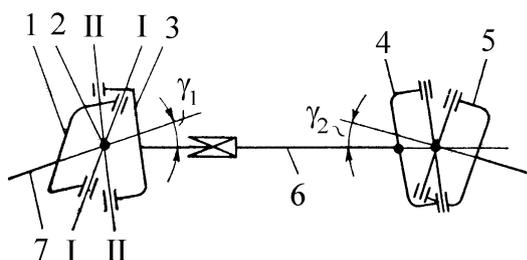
Схема карданной передачи: 1, 3, 4, 5 – вилки карданов; 2 – крестовина; 6 – промежуточный вал; 7 – ведущий вал
